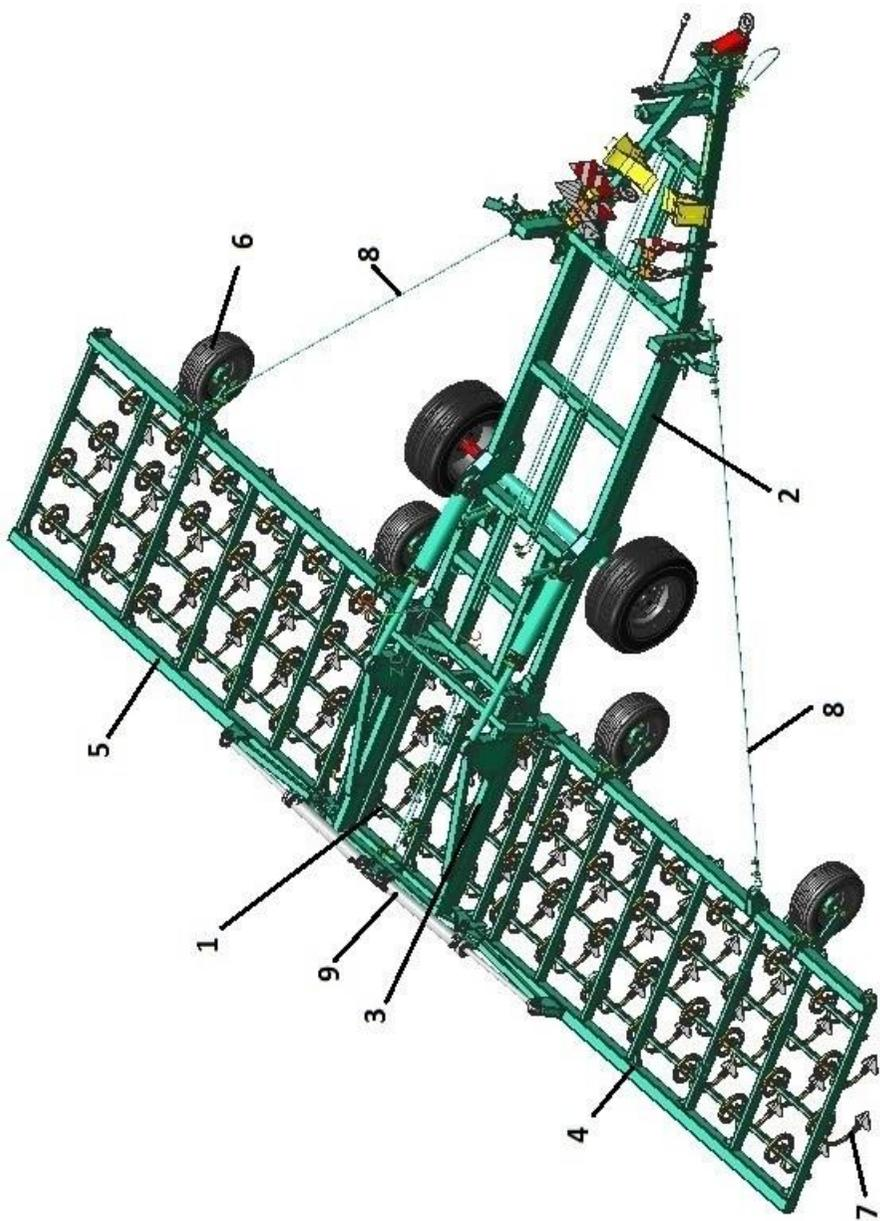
Общий вид культиватора КРМ-8ПЕ в рабочем положении
